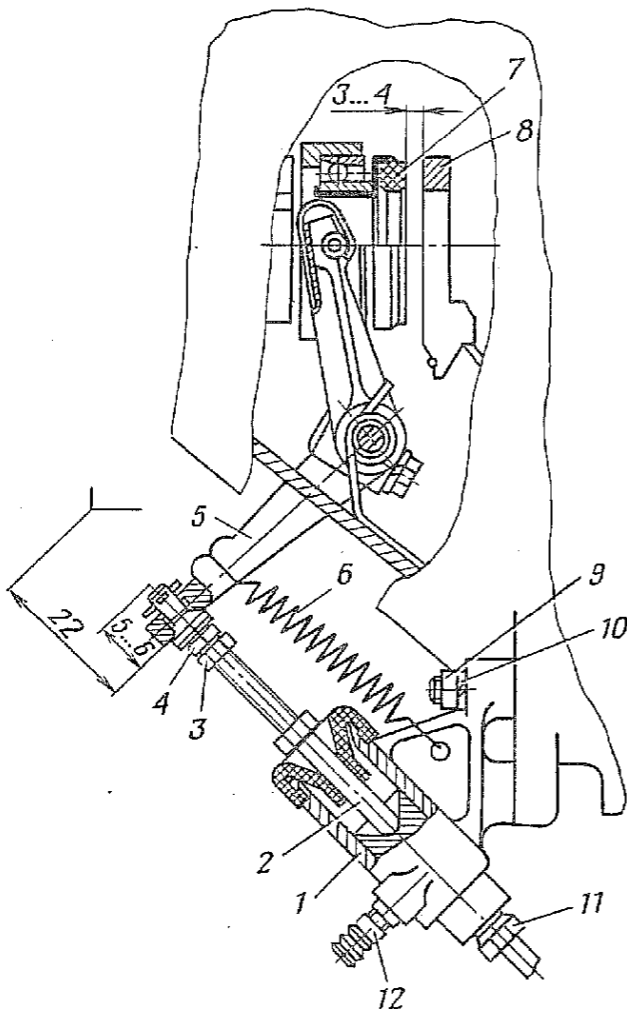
Регулировка свободного хода привода выключения сцепления:
